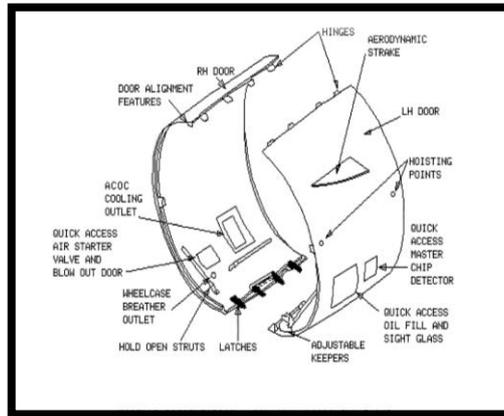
Cubiertas del Fan Puertas (LH – RH)
